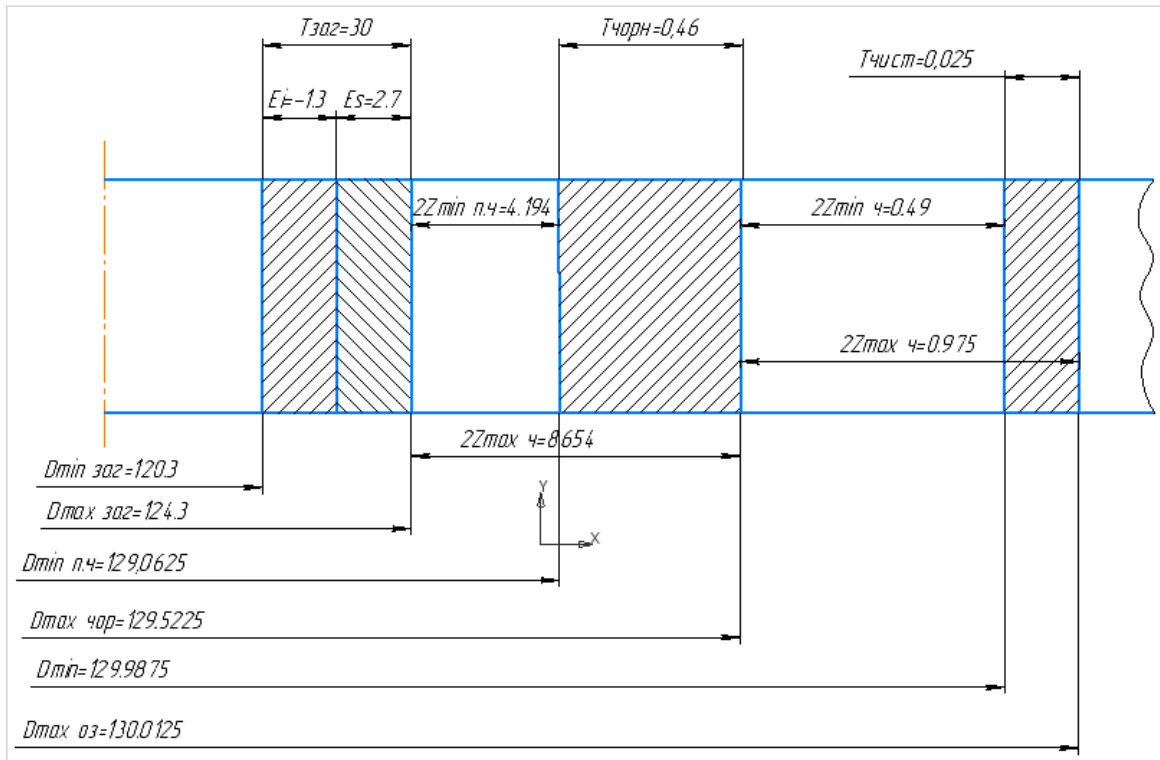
Схема розташування допусків та припусків
